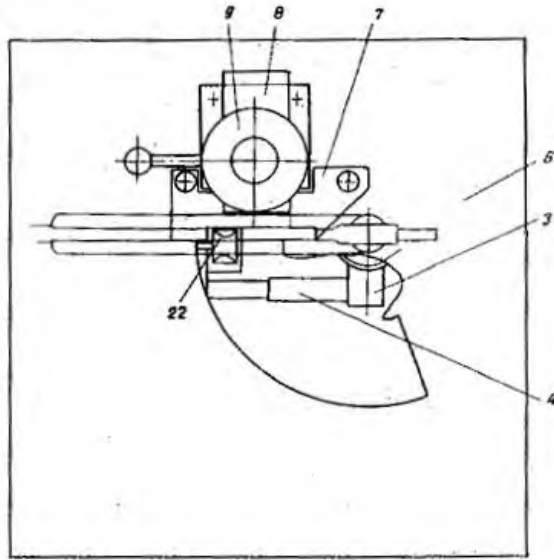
Пристрій для контролю зусиль на шарнірах кронциркулів, вид зверху
